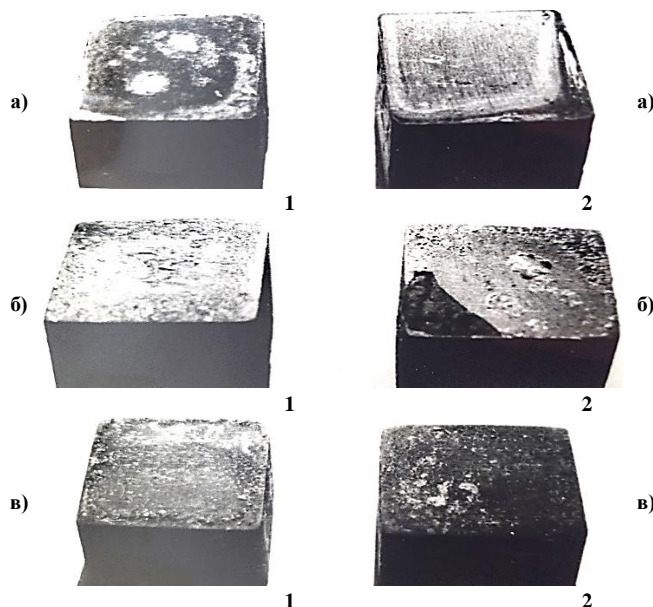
Фотография образцов, изготовленных из обрабатываемого материала сталь 45.
